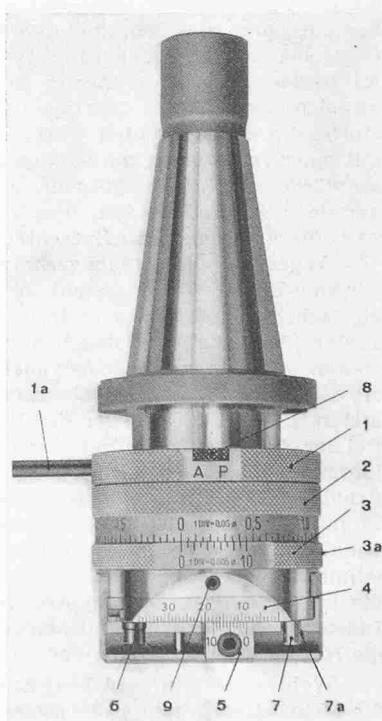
(rechts). Präzisions-Plan- und Ausdrehwerkzeug auf Schäublin-Fräsmaschine Typ SV 53
